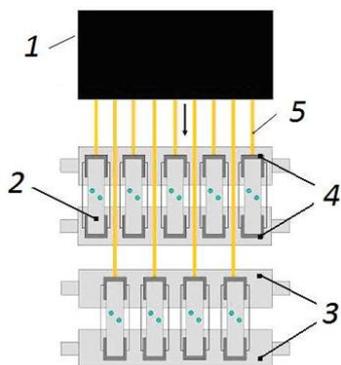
Расположение пневмоцилиндров в конструкции вытяжного устройства при вытягивании прутков малого диаметра (вид сверху):
